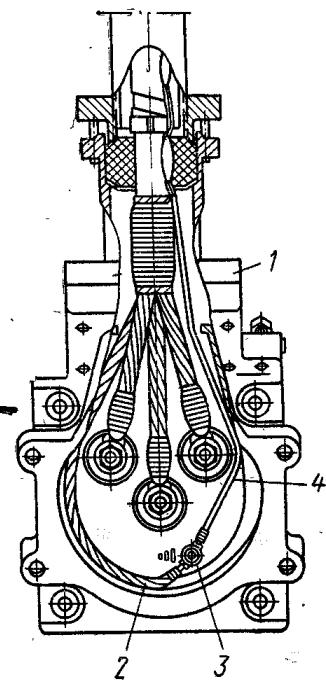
Общий вид смонтированной вводной коробки (без крышки) взрывозащищенного электродвигателя серии ВАО 4-го — 9-го габаритов.
